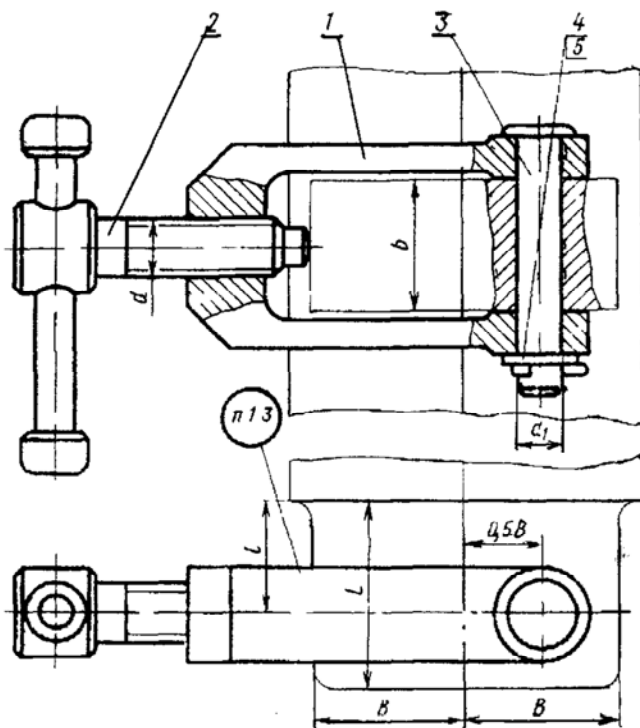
Винтовой замок для скрепления створчатых кокилей:
